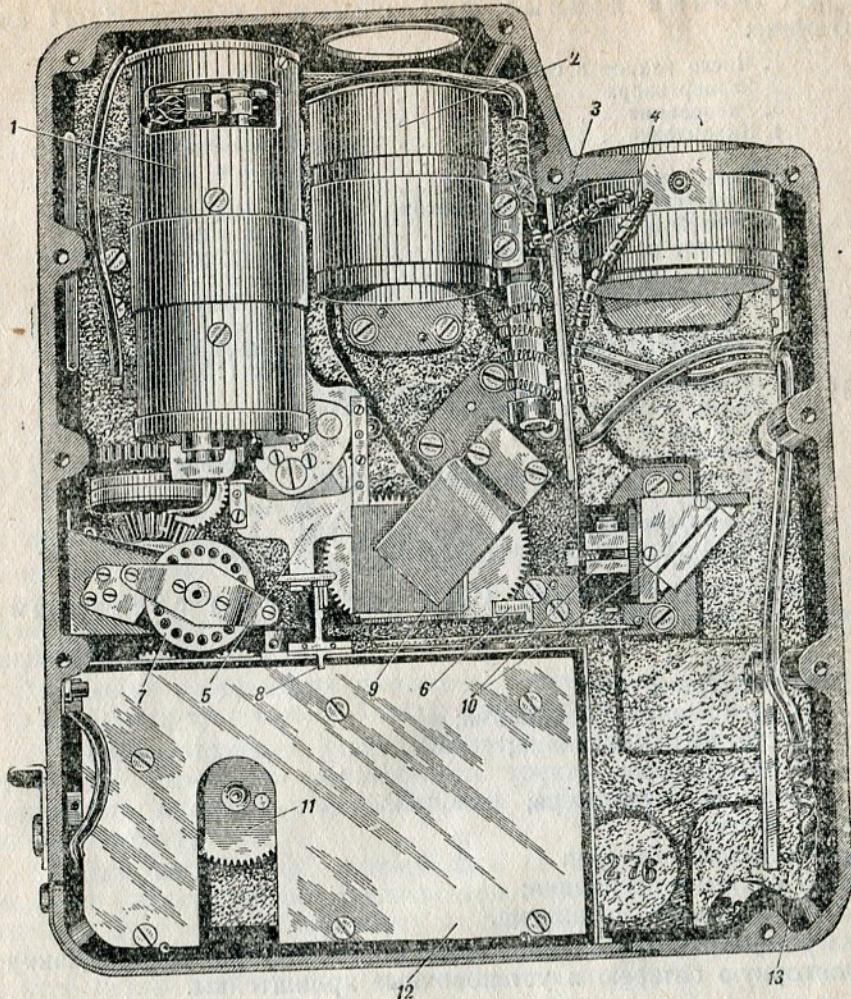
Расположение механизмов фотокинопулемета в его корпусе
